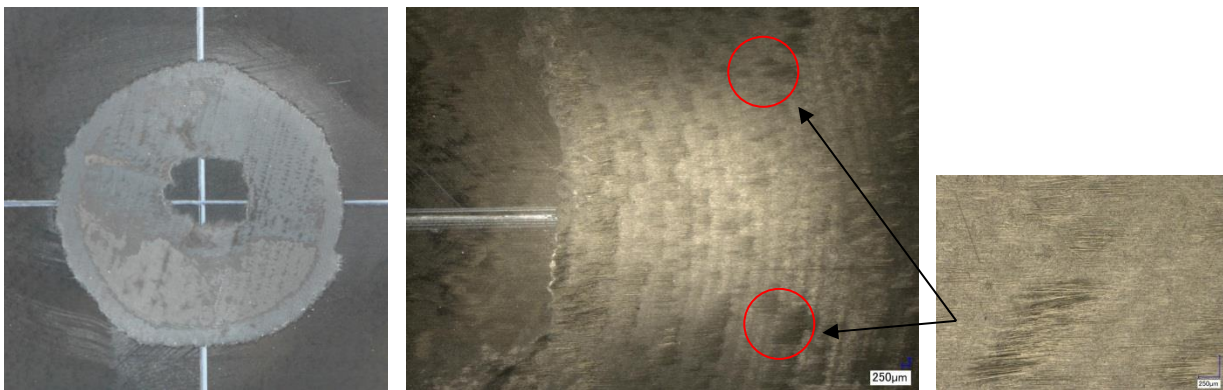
Gefräste Probe mit 190 min/140°C Anhärtung
